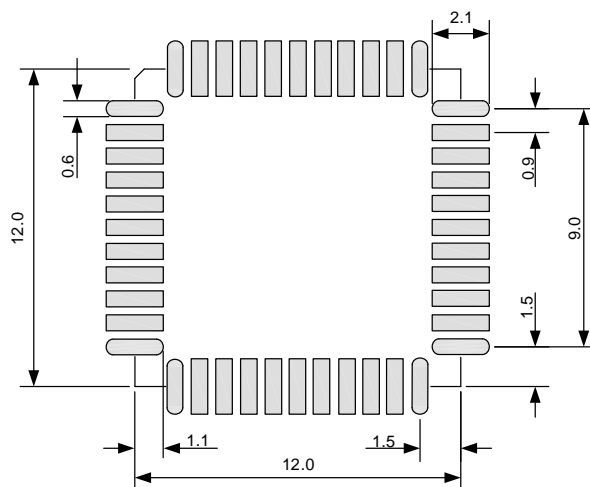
ZM5955S 推荐 PCB 封装尺寸
